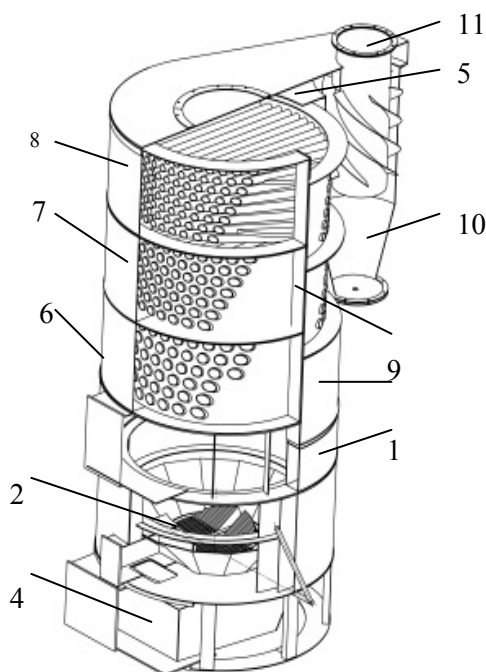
Общий вид теплообменного модуля Е.Н.Воронова: 1 — корпус; 2 — конусообразное топочное устройство; 3 — загрузочное кольцо; 4 — под топочного устройства; 5 — коллектор дымовых газов; 6 — нижний модуль нагревательных элементов с диаметром трубок $d_{тр} = 60 \times 4,5$ мм; 7 — средний модуль нагревательных элементов с диаметром трубок $d_{тр} = 52 \times 3,5$ мм; 8 — верхний модуль нагревательных элементов с диаметром трубок $d_{тр} = 42 \times 3,5$ мм; 9 — сборно-распределительные водяные коллекторы («водяная рубашка»); 10 — циклон газоочистки; 11 — выход дымовых газов
